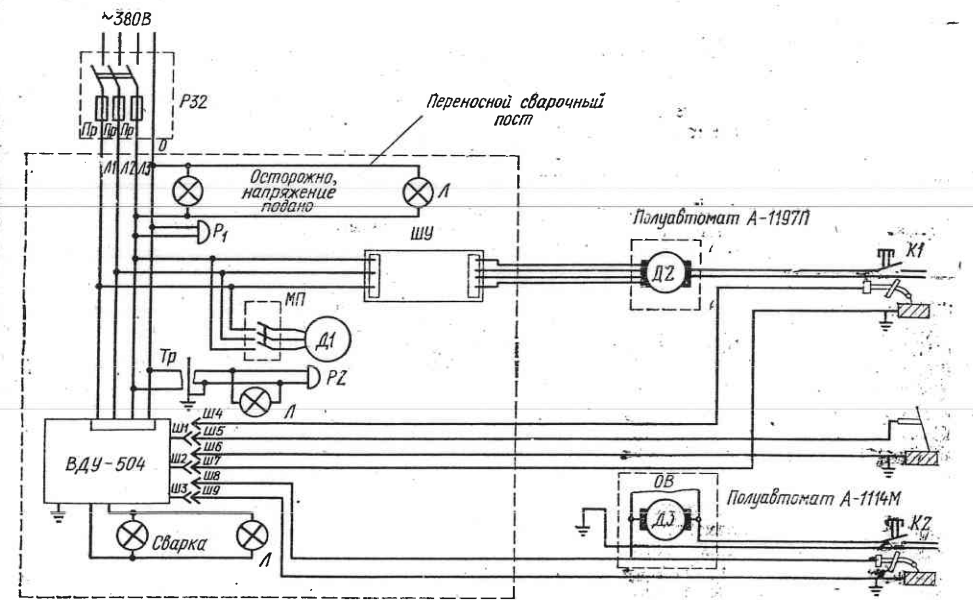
Принципиальная электрическая схема инвентарного переносного поста для полуавтоматической сварки
